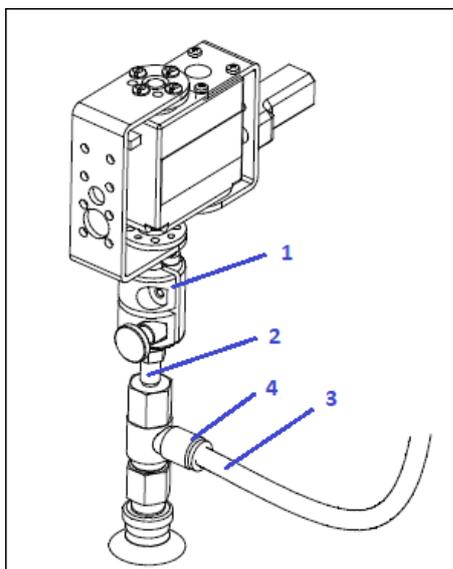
Поворотный модуль инструмента с присоской вакуумного захвата, где 1 – муфта поворотного модуля инструмента; 2 – хвостовик присоски; 3 – полиуретановая трубка для компрессора; 4 – фитинговый держатель
